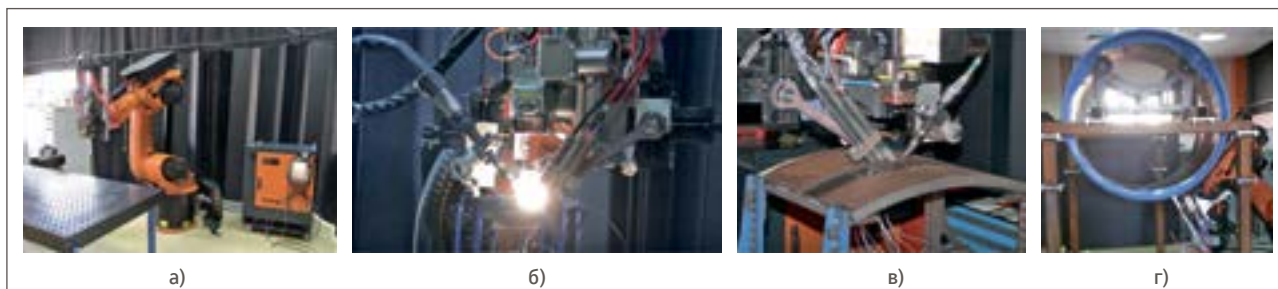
Отработка технологии на роботизированном комплексе: а) внешний вид роботизированного комплекса; б) сварка пластин; в) сварка сегментов; г) сварка труб
